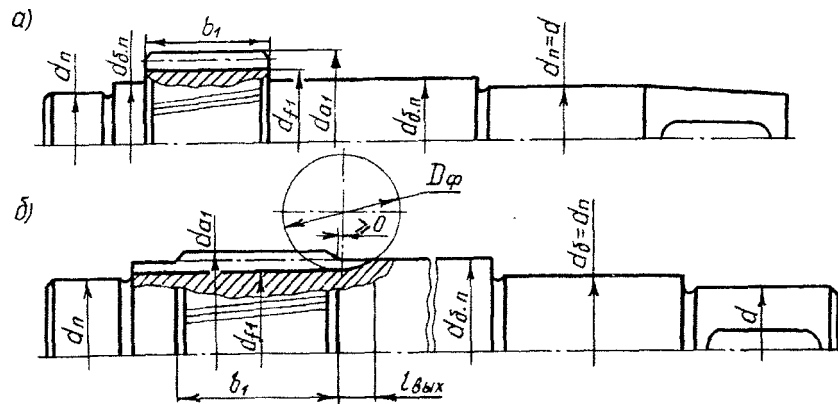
Варианты конструкции быстроходного вала двухступенчатого цилиндрического редуктора, выполненного по простой развернутой схеме: d - диаметр конца вала; d_n - диаметр отверстия внутреннего кольца подшипника; d_a - диаметр буртика вала для упора детали; $d_{δ.n}$ - диаметр буртика (заплечика) вала для упора внутреннего кольца подшипника; $D_φ$ - диаметр фрезы; $l_{вых}$ - длина участка для выхода фрезы
